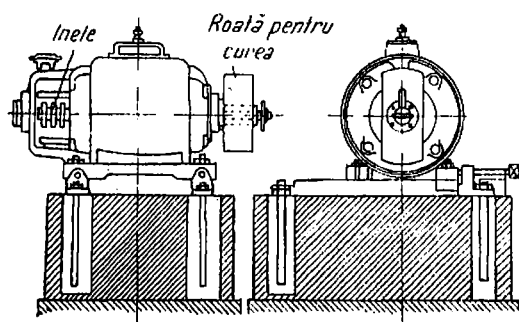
Motor asincron cu rotor bobinat și inele.
